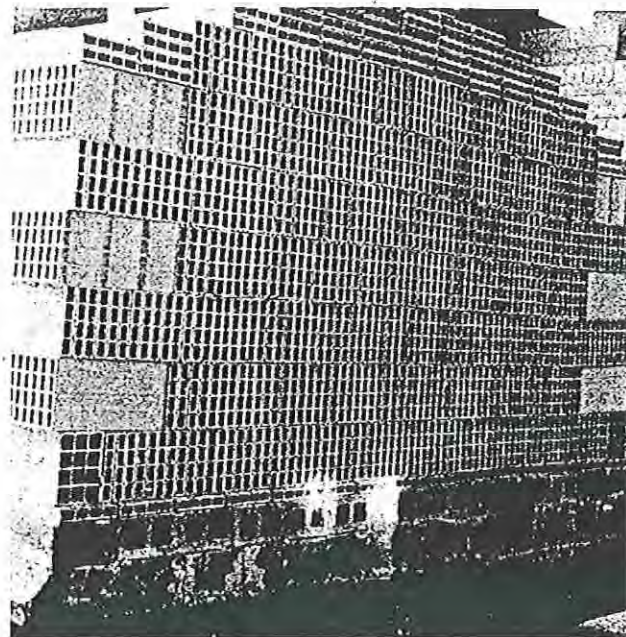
Empilage de briques sur un wagon de four tunnel circulant sur une voie extérieure au four.
